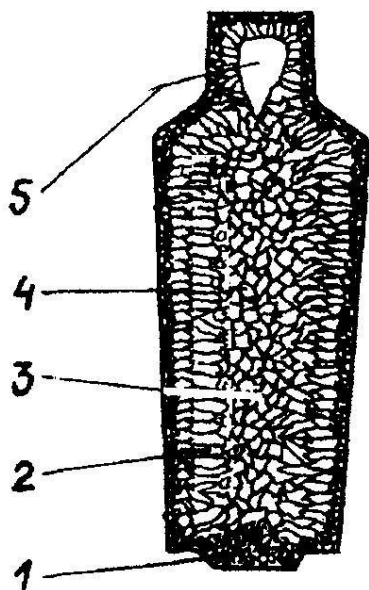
Будова зливка зі спокійної сталі: 1 - дрібнокристалічна нижня частина зливка; 2 - стовпчасті кристали; 3 - центральна зона великих кристалів; 4 – дрібнокристалічна поверхнева зона; 5 - усадкова порожнина
